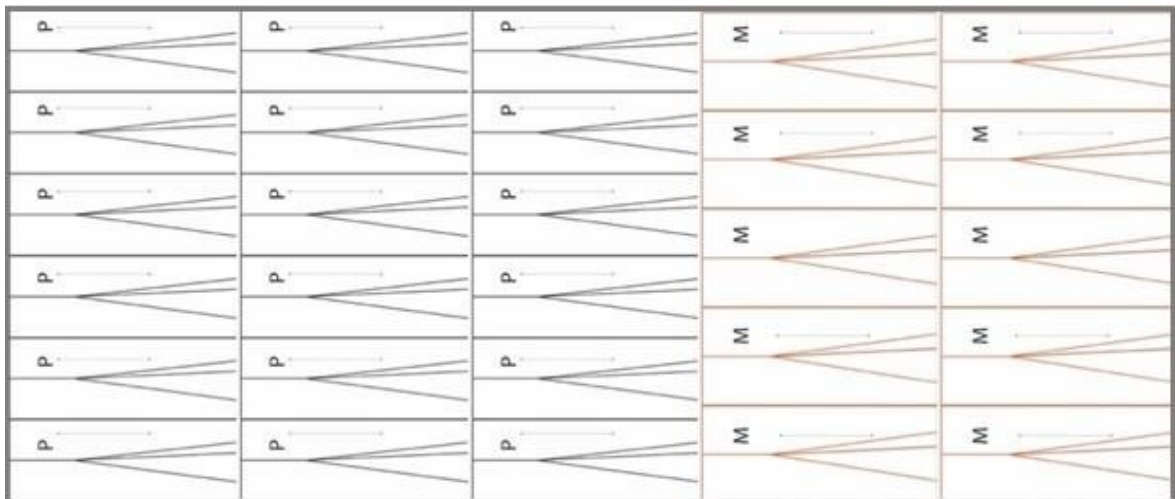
plano de corte em metragem ampla de tecido. Fonte: elaborado pelos autores.
